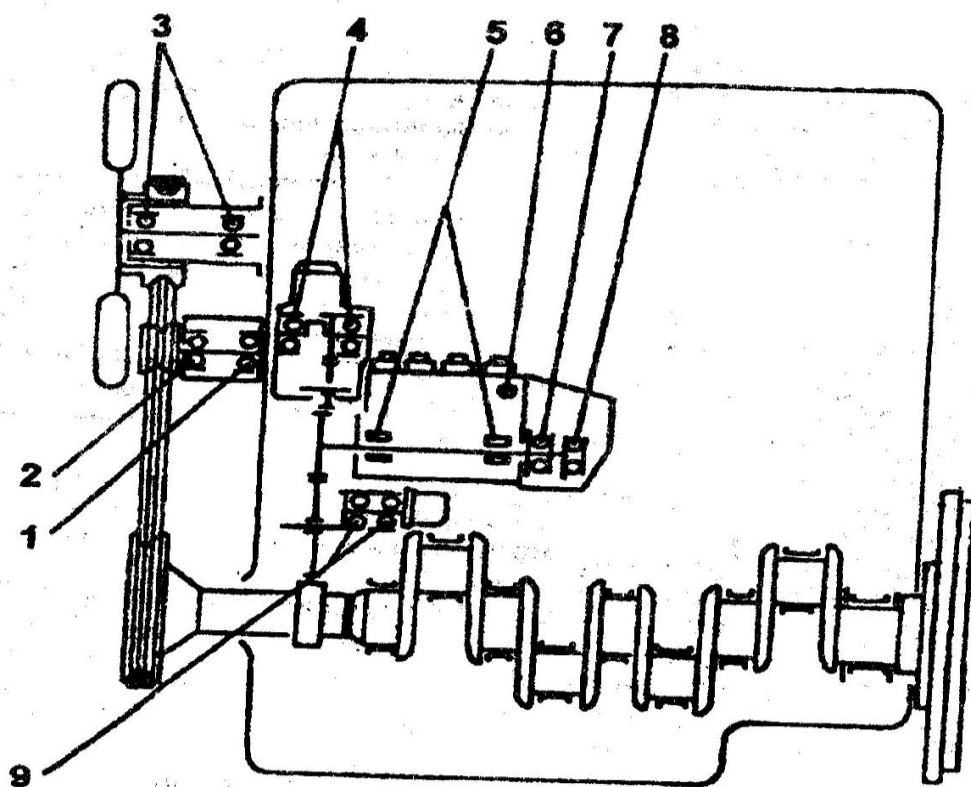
Схема расположения подшипников качения двигателя комбайна КЗС-3
